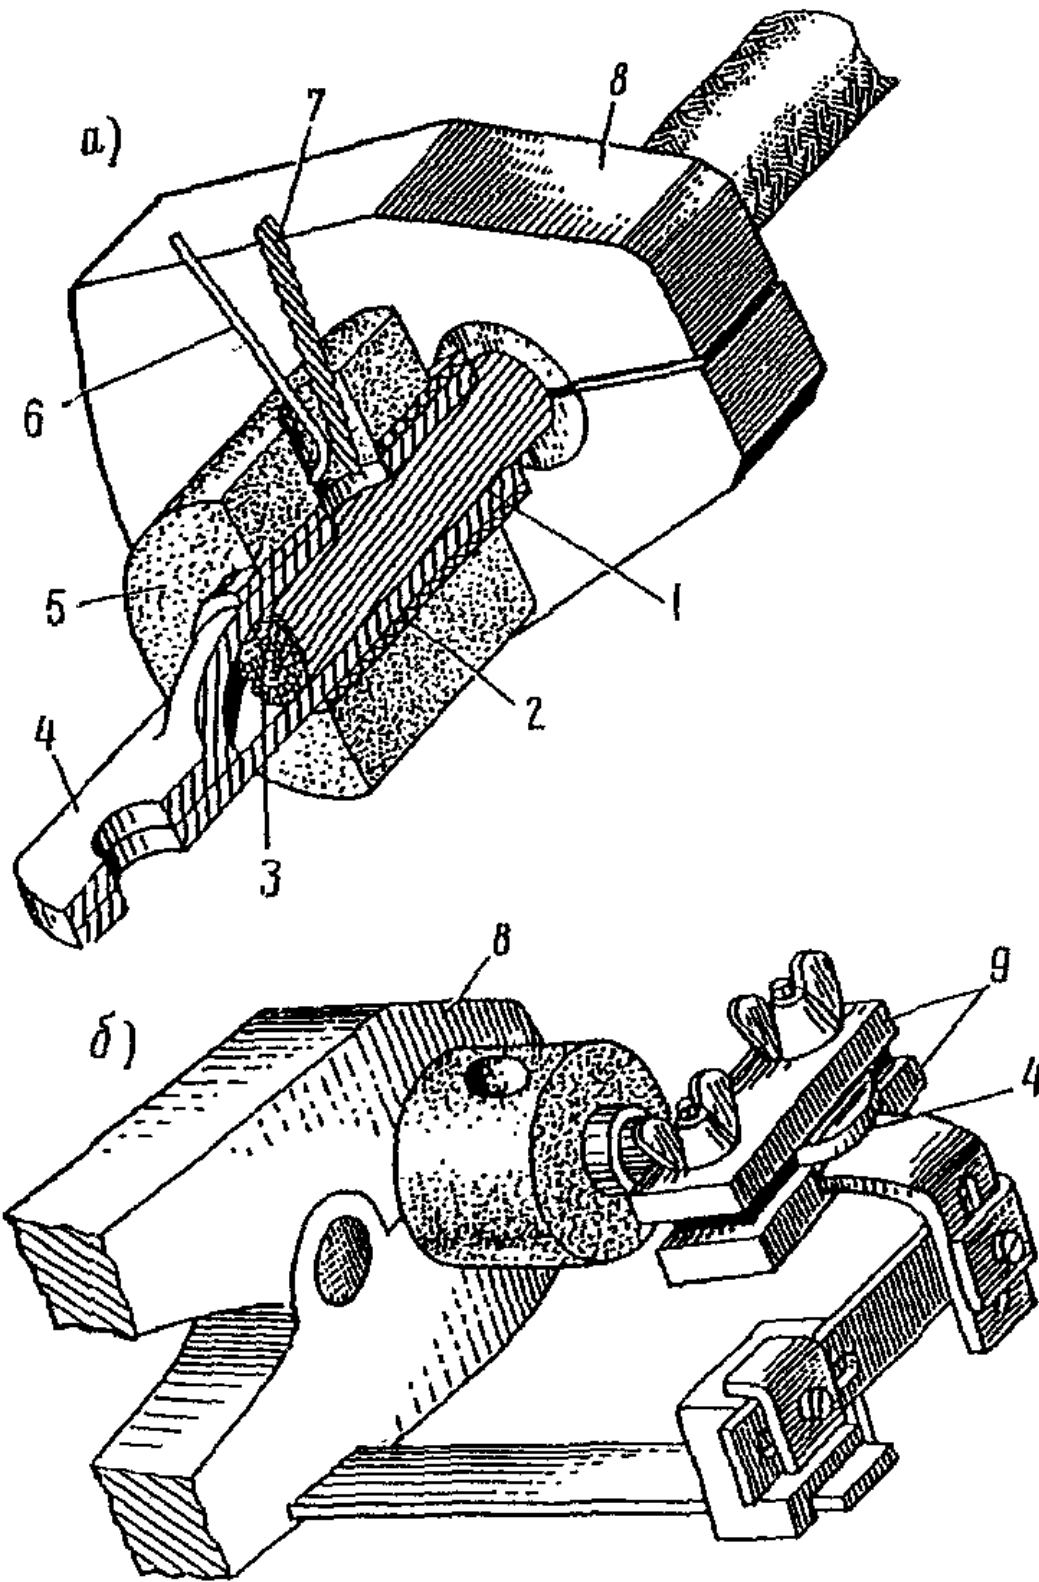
Оконцевание жил кабелей путем приварки трубчатого наконечника: а - установка и уплотнение термитного патрона; б - общий вид приспособления для приварки наконечника; 1 - асбестовый шнур; 2 - кокиль; 3 - жила кабеля; 4 - наконечник; 5 - муфта термитного патрона; 6 - проволочная мешалка; 7 - присадочный алюминиевый пруток; 8 - охладитель; 9 - зажим
